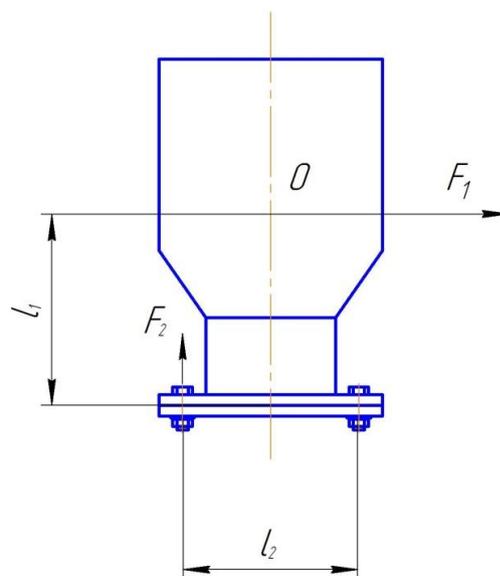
Схема для расчета резьбовых соединений крепления электропневматической сеялки
